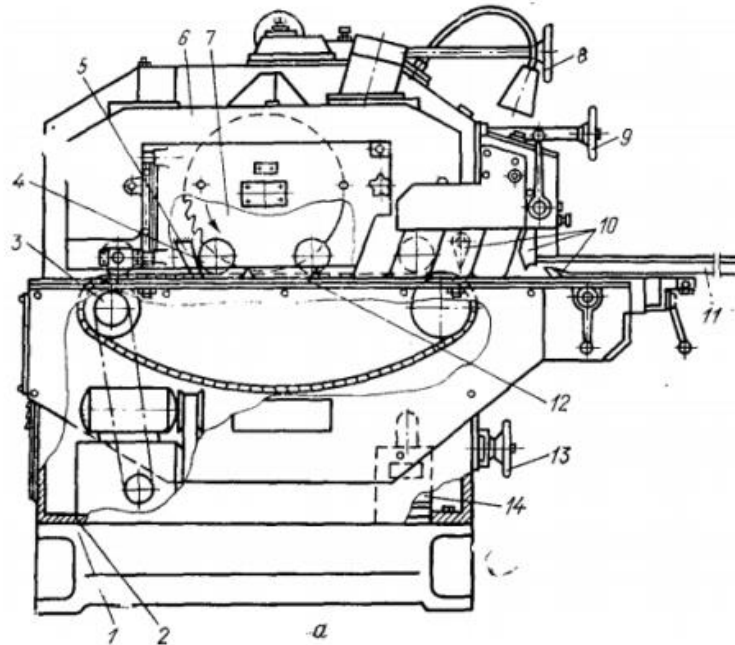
Конструктивний склад деревообробного верстату ЦКБ-40
